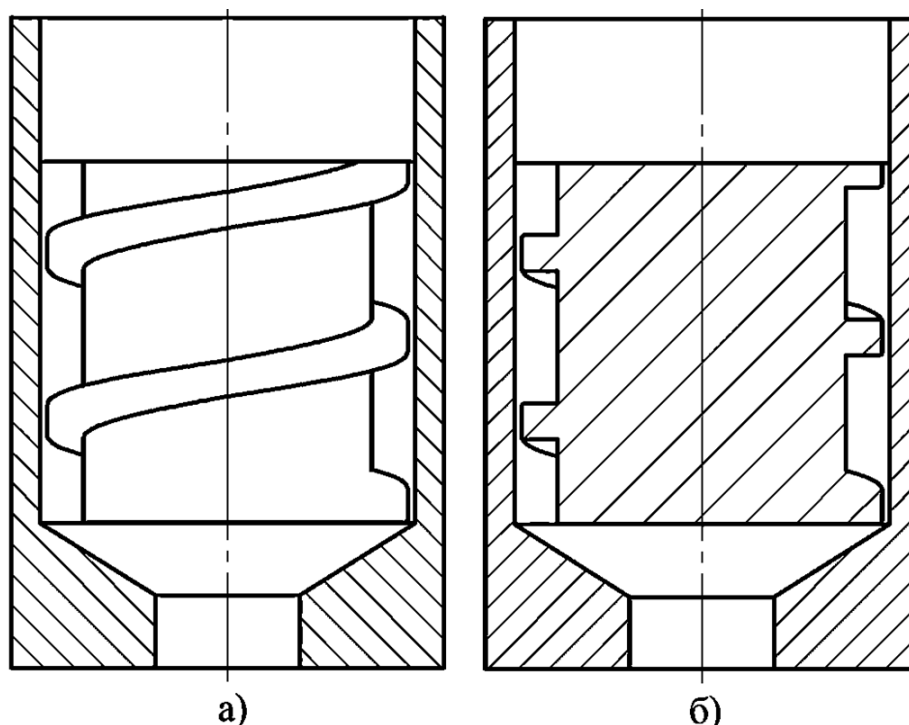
Схема открытой шнековой центробежной форсунки:
